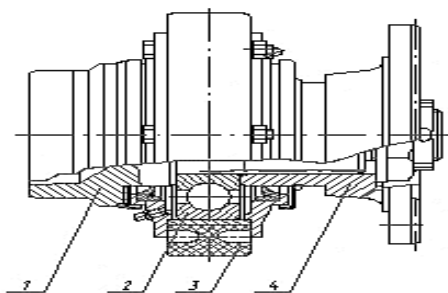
Промежуточная опора карданной передачи 650118-2205006-001: 1 – шлицевый конец; 2 – шариковый подшипник; 3 – резиновый виброизолятор; 4 – соединительный фланец
